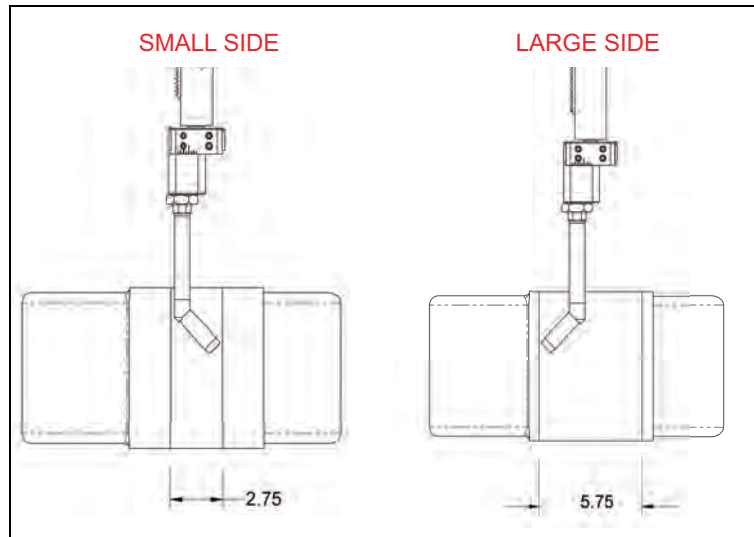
AJUSTE DE ORIENTACIÓN Y POSICIÓN DEL SOPLETE (LADO PEQUEÑO A LA IZQUIERDA, LADO GRANDE A LA DERECHA)
